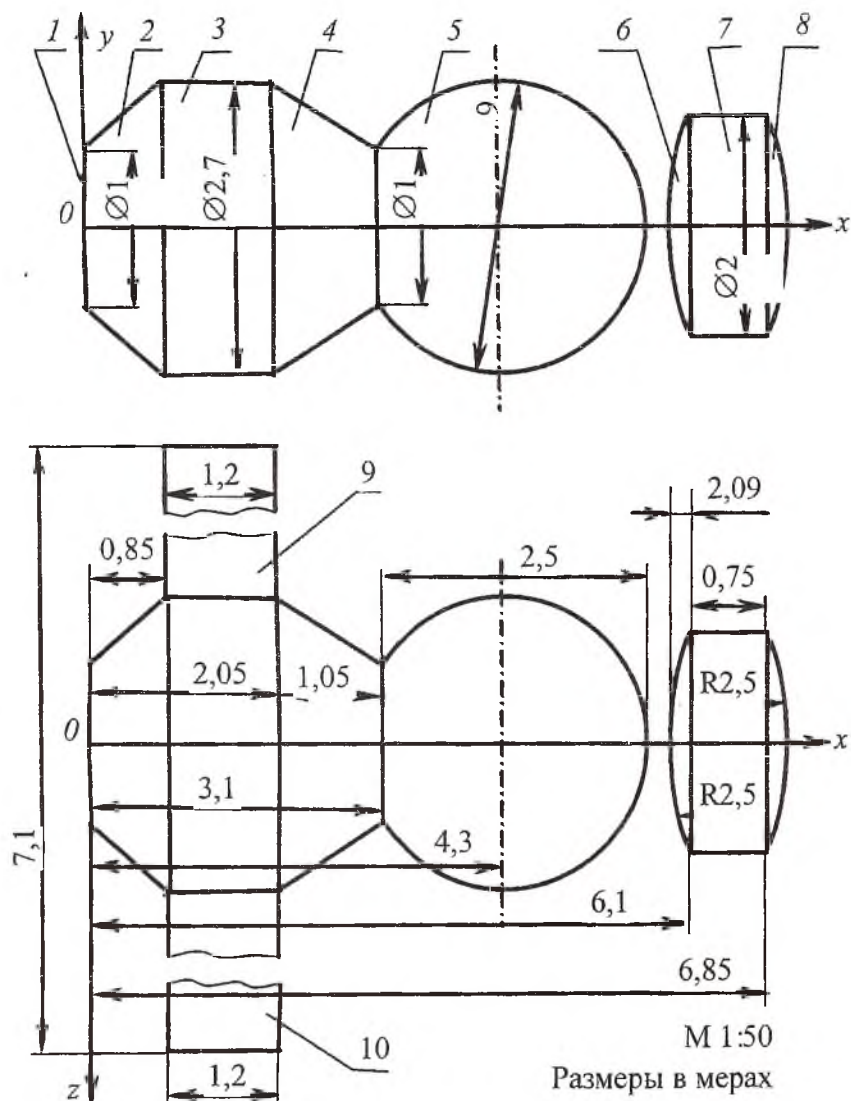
Габаритный чертёж КА UMPRIM :1 - доньшко;
